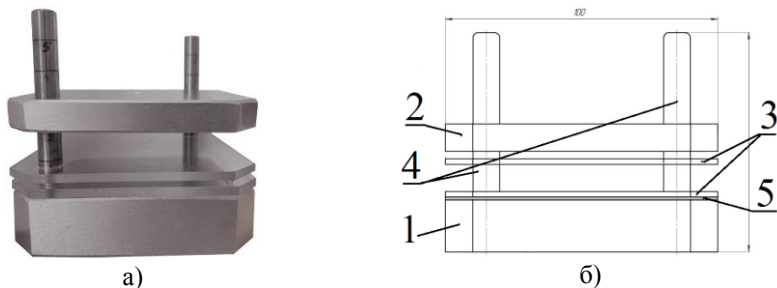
а) промышленный образец б) Эскизный чертеж устройства с обозначением конструктивных элементов: 1 – металлическое основание устройства; 2 – металлическая съемная пластина с загрузочным отверстием; 3 – стеклянная съемная пластина; 4 – вертикальная направляющая; 5 – фотошаблон с диаметральной шкалой в виде прицела
